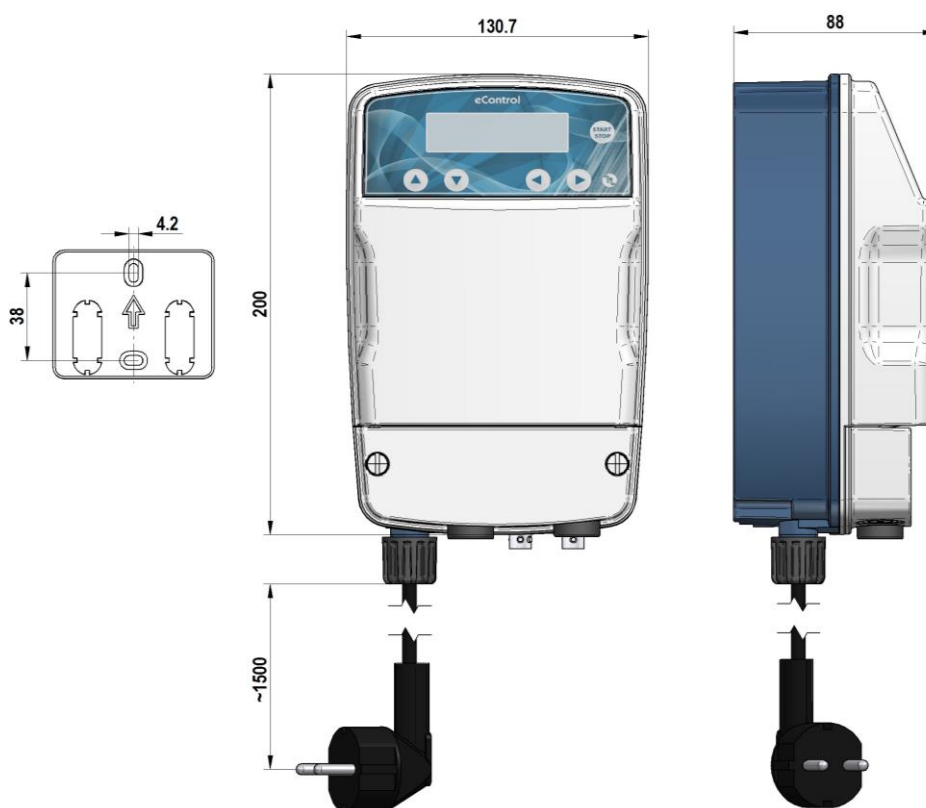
eControl instrument en wandmontageplaat (afmetingen in mm.).
